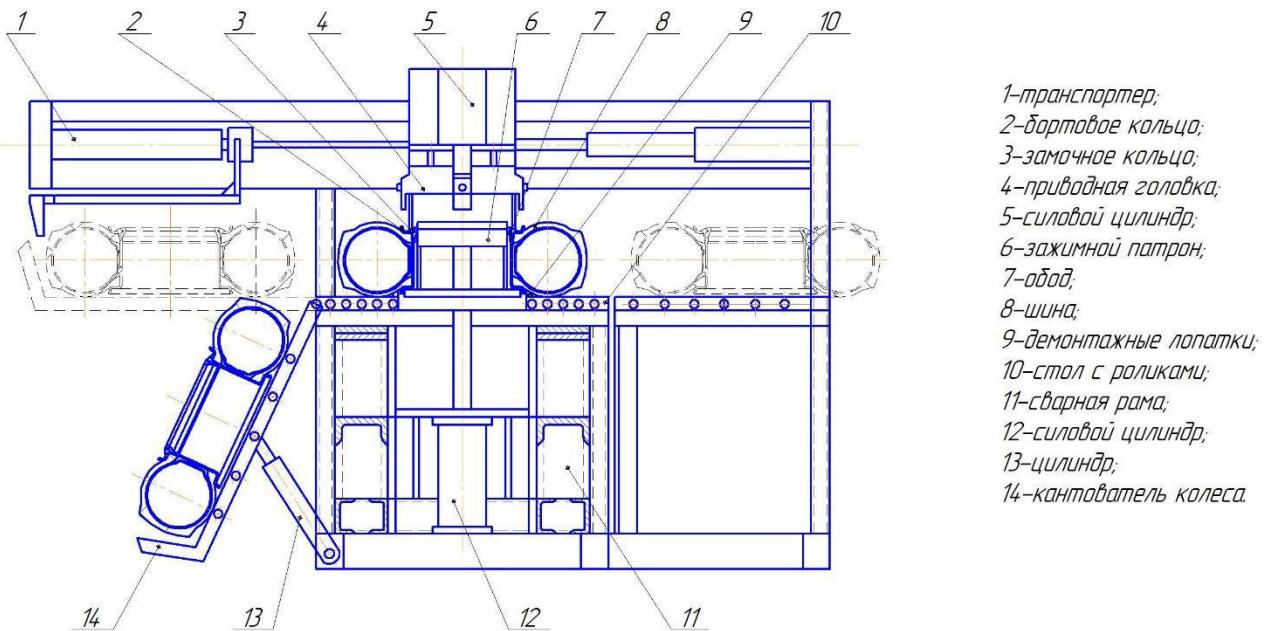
Стенд для демонтажа шины колеса транспортного средства
